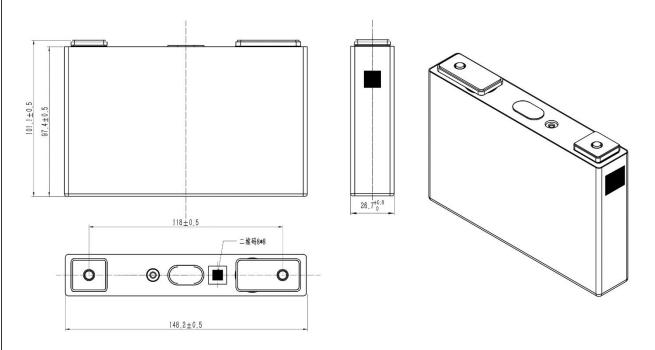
电池尺寸图 Figure A.1 Cell Dimensional Drawing
